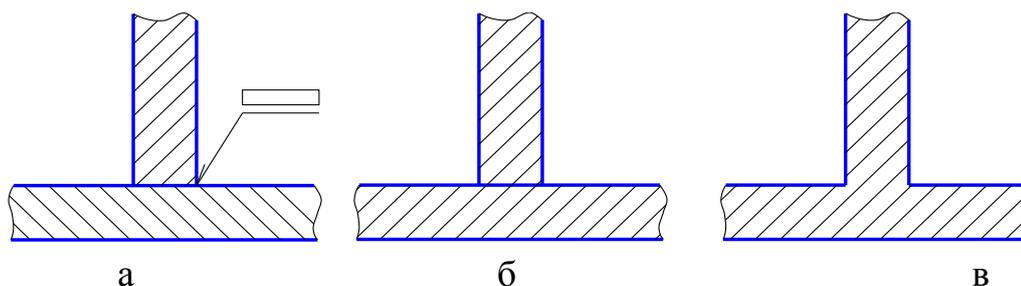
Примеры штриховки сварных соединений
